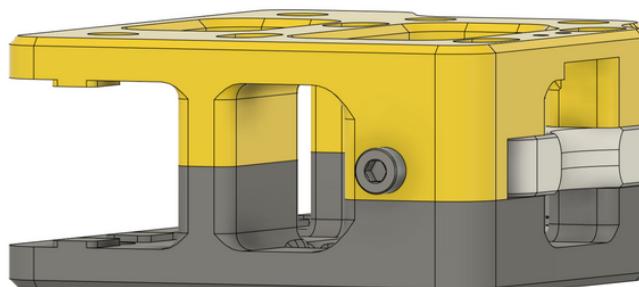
Fijación de la pieza [a]_belt_tensioner.
